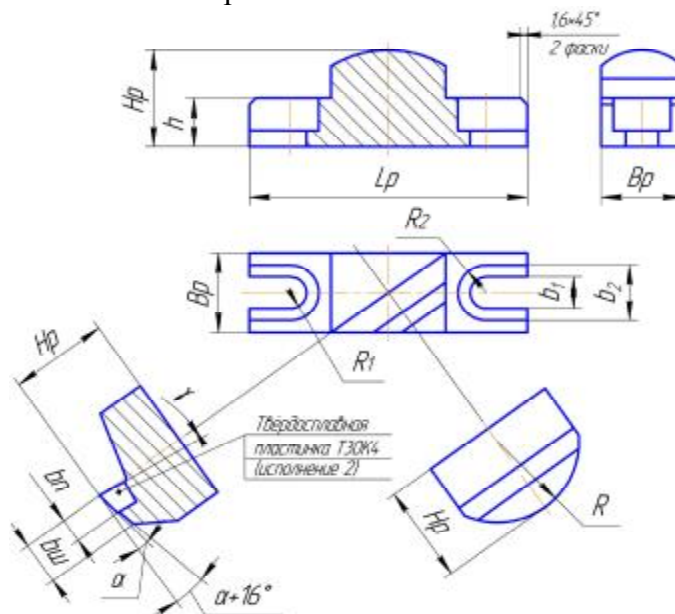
Конструкция вставного зуба-резца, оснащённого твёрдосплавной пластинкой
